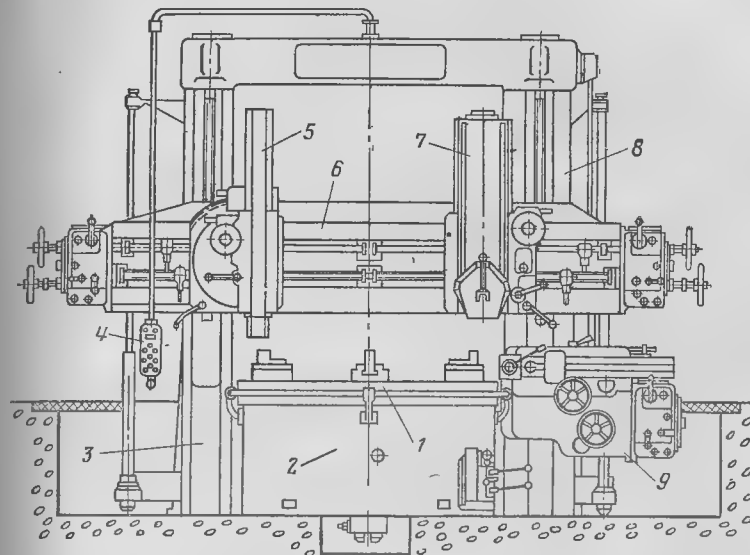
Общий вид тяжелого карусельного станка модели 1553.
